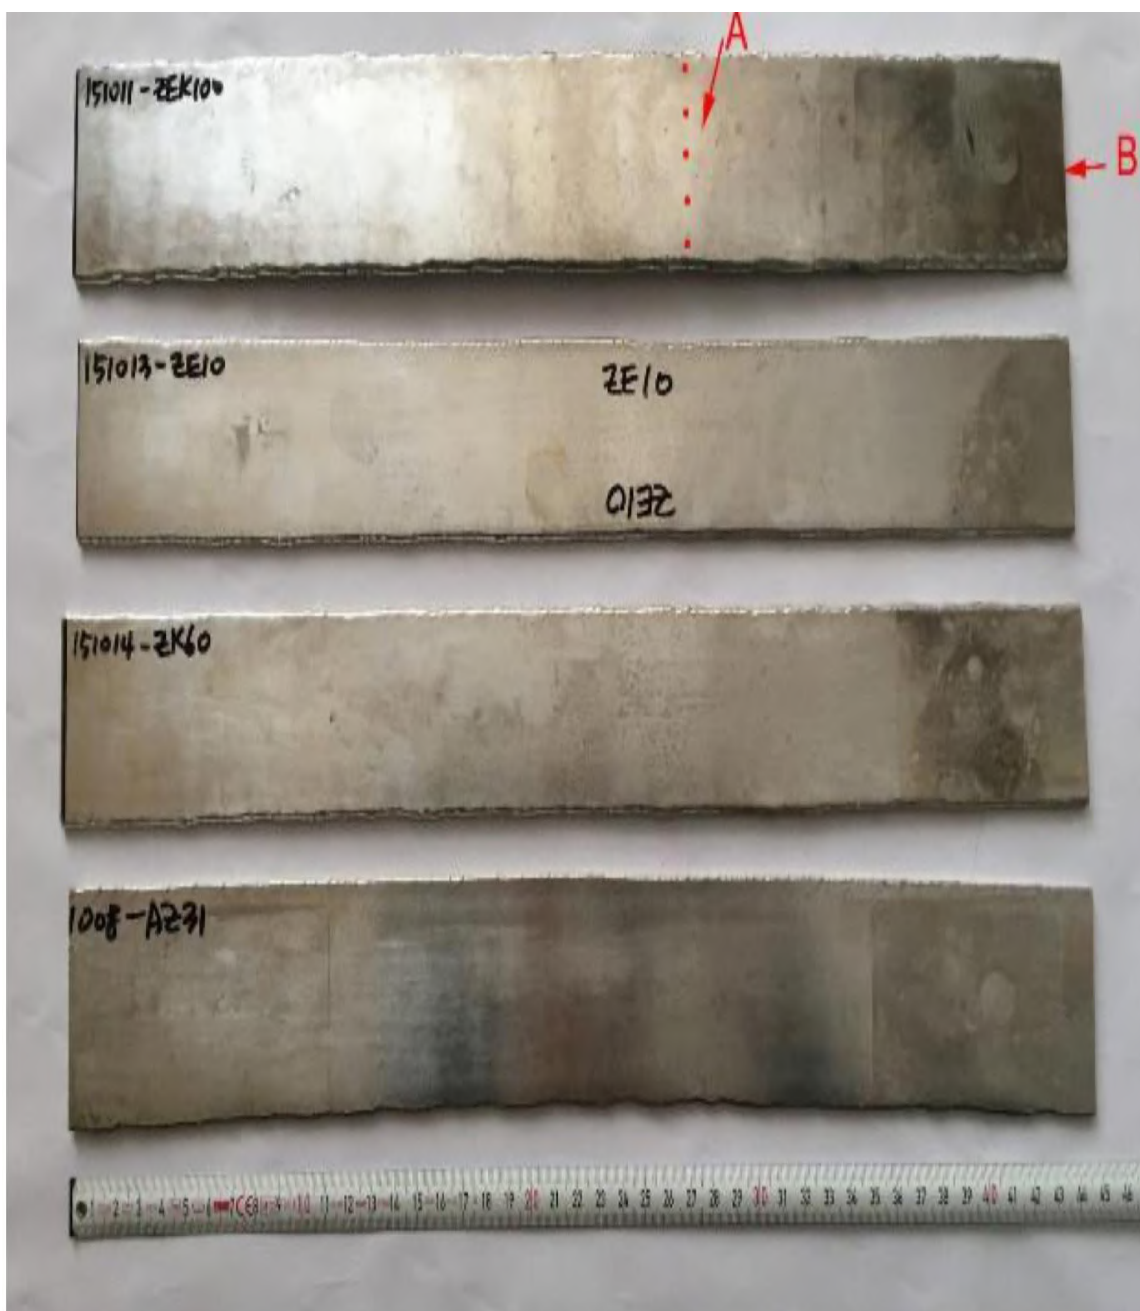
Внешний вид образцов литья на двухвалковых машинах AZ31, ZK60, ZE10 и ZE100 (а) и обозначения главных осей
